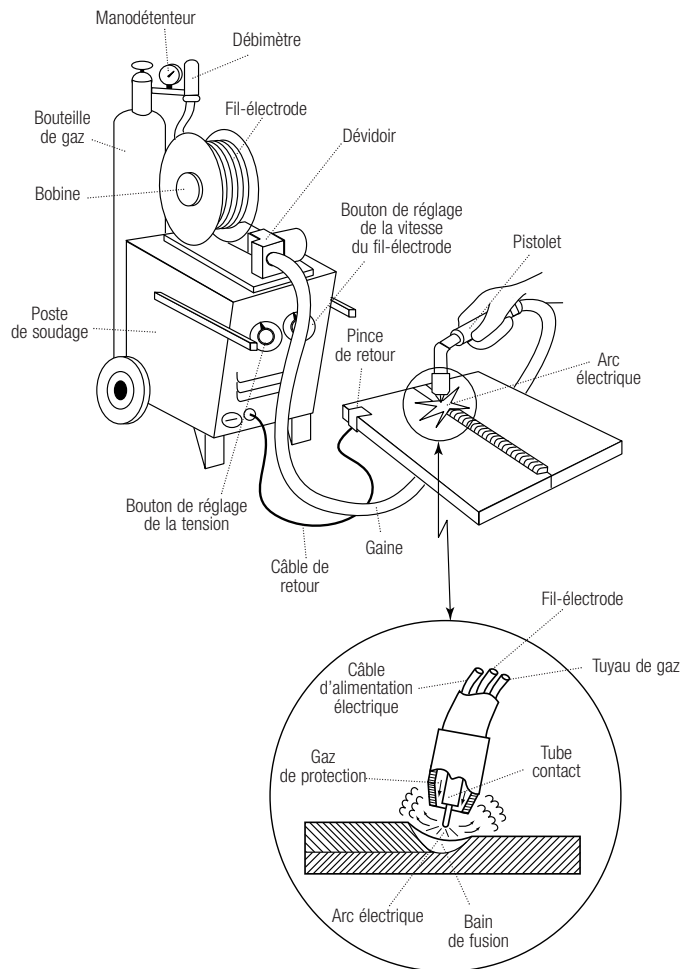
Arrangement typique de soudage semi-automatique GMAW
